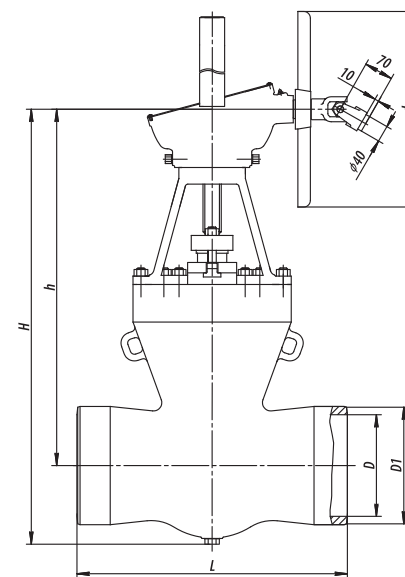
Задвижка DN150...400 с коническим редуктором
